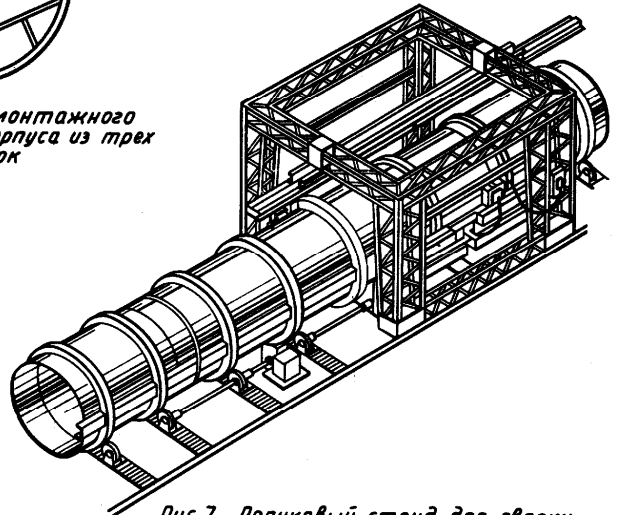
Роликовый стенд для сварки кольцевых и продольных швов на монтаже
